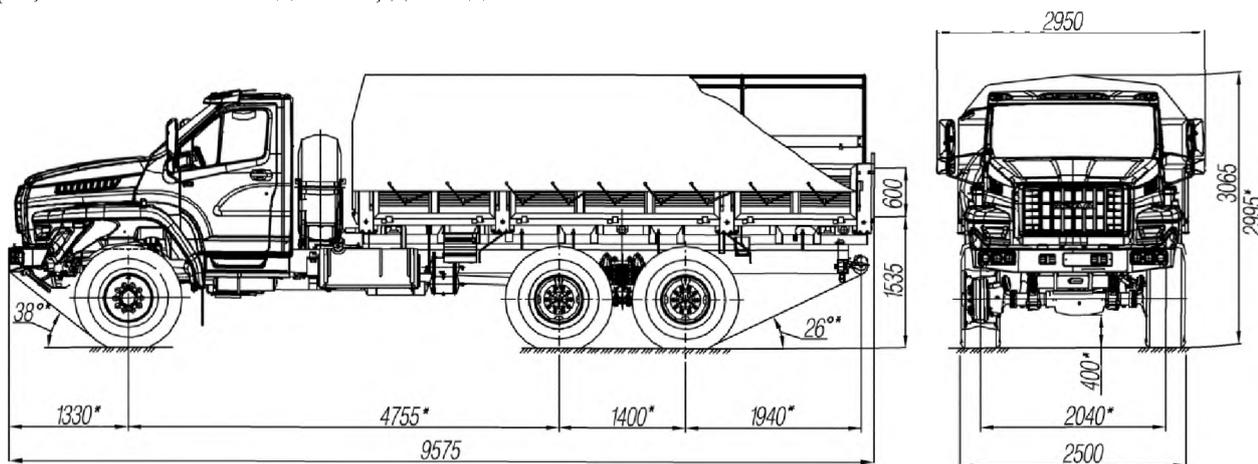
Габаритные размеры автомобиля Урал-4320-5911-72/74
